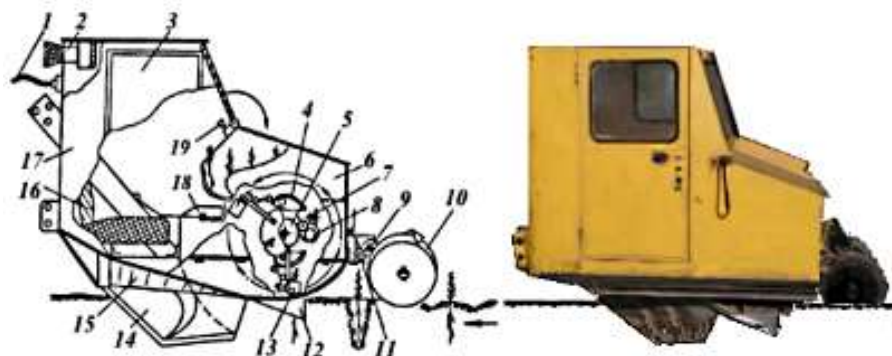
Схема лесопосадочной машины ЛМД-21: 16 – сиденье; 1 – электропривод; 2 – вентилятор с фильтром; 3 – дверь; 4 – лекало раскрывателя захватов; 5 – зубчатое колесо вала посадочного аппарата; 6 – бункер для посадочного материала; 7 – бортовая электросеть; 8 – электродвигатель постоянного тока; 9 – крестовина; 10 – прикатывающие катки; 11 – храпово-пружинный механизм регулирования давления катков на почву; 12 – заделывающие клинья; 13 – захват; 14 – сошник; 15 – опорная пластина; 16 – сидение са- жальщика; 17 – кабина; 18 – приемный столик для семян; 19 – панель управления элек- троприводом
